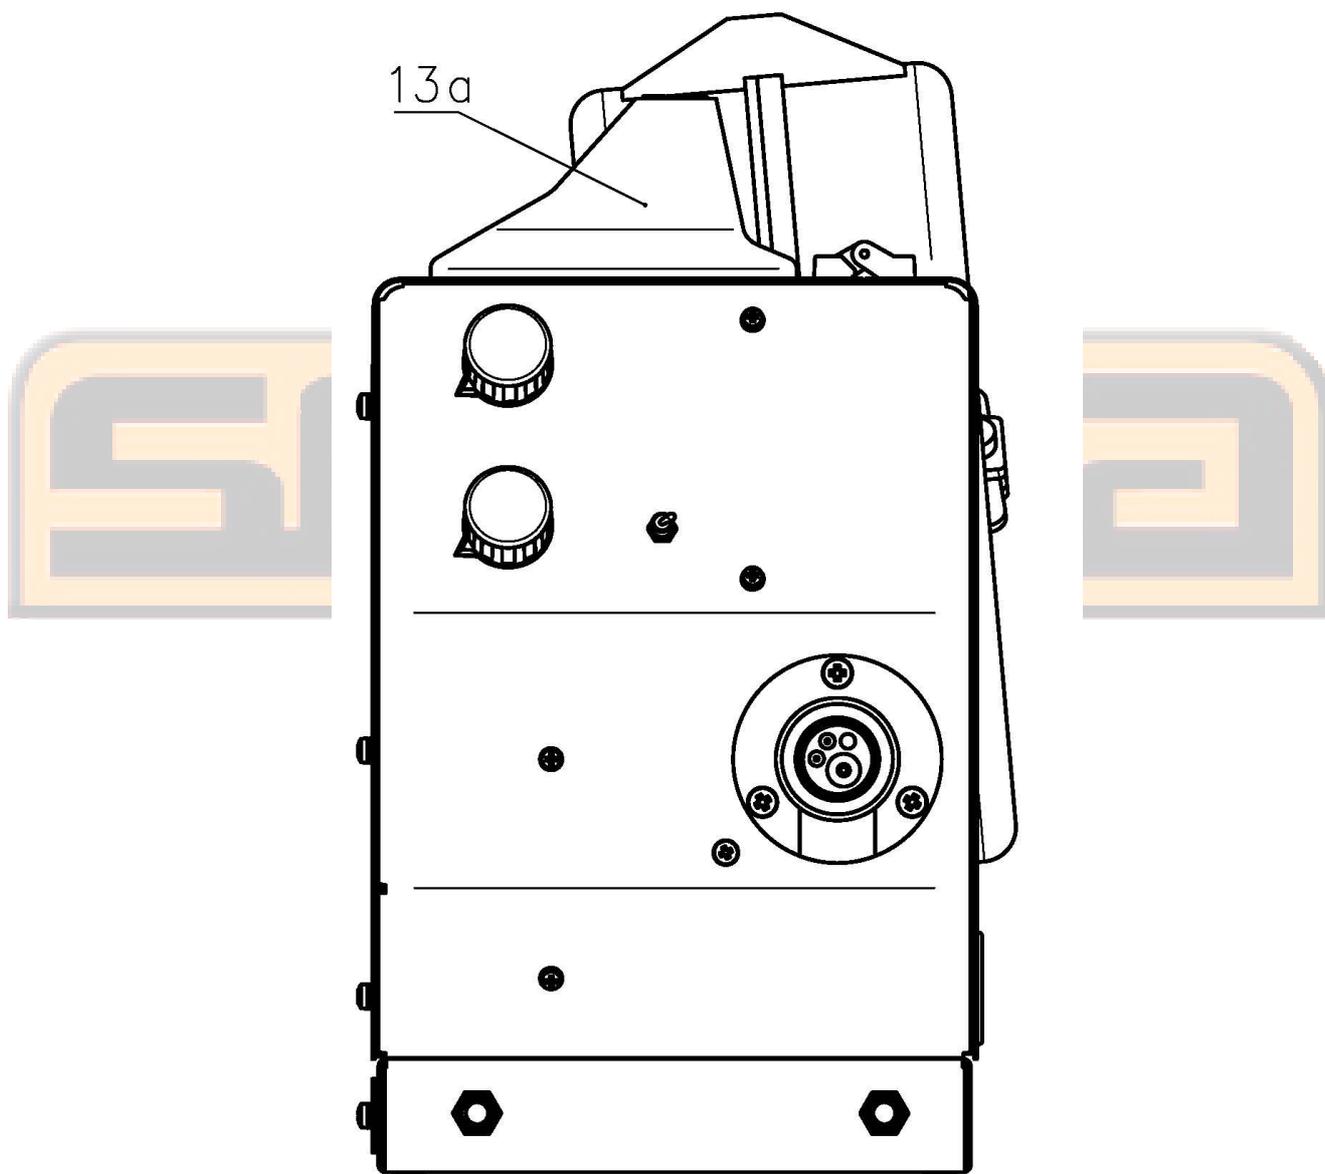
а (лист 1 из 2) – Внешний вид подающего механизма без металлической защитной рамы
